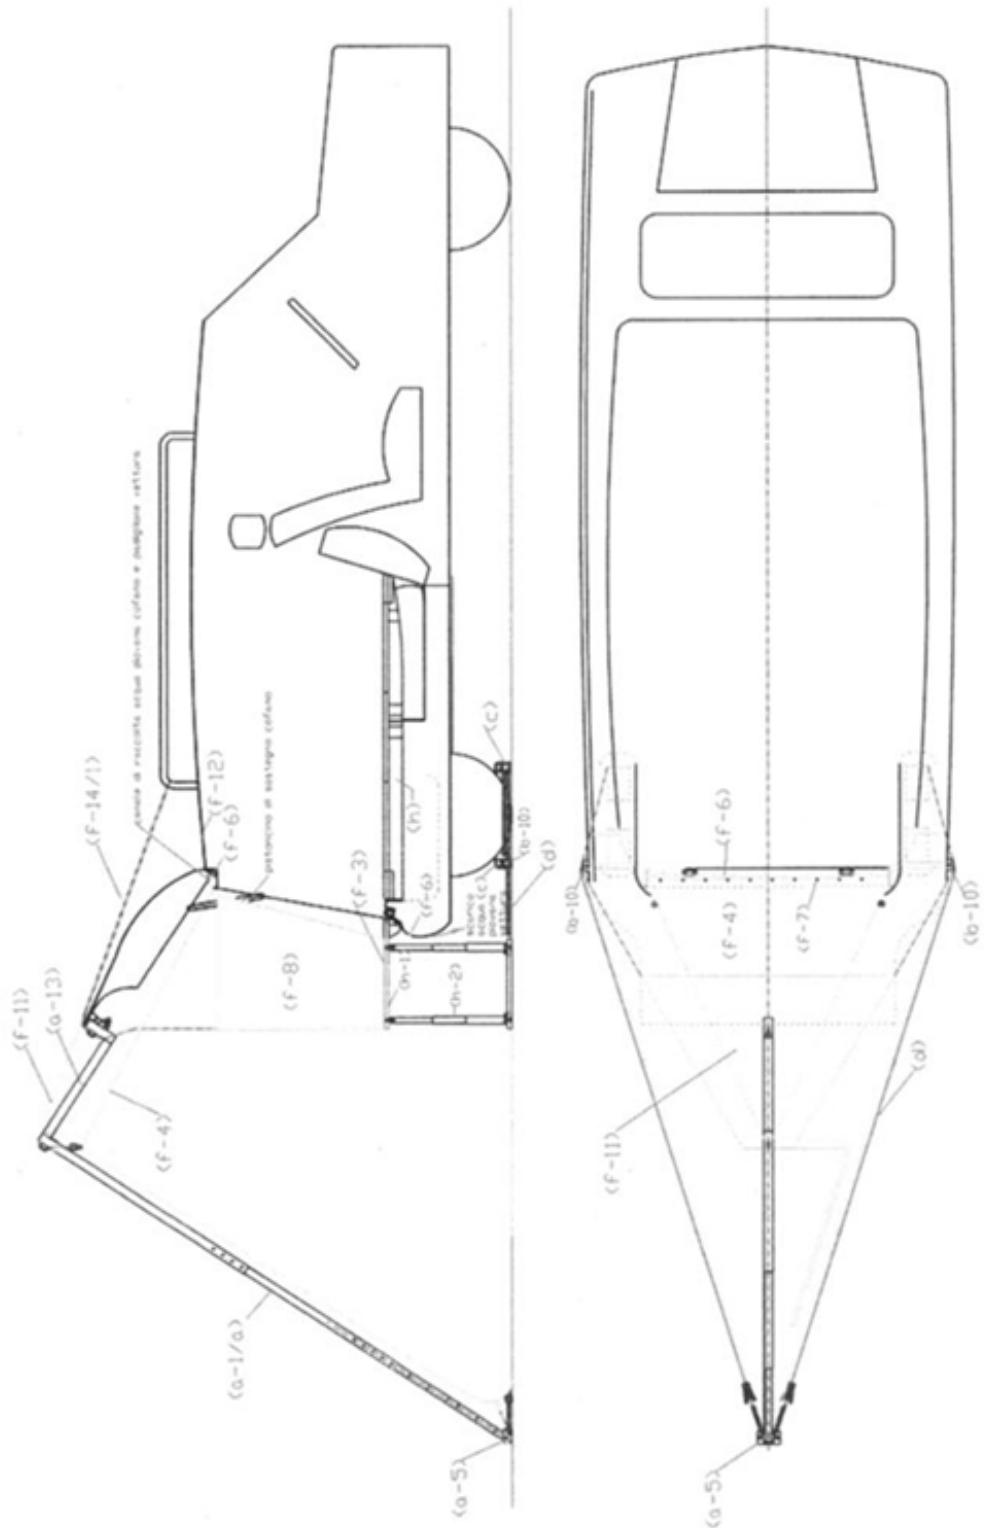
SEZIONE LONGITUDINALE E VISTA IN PIANTA TENDA CANADESE CON PROLUNGA PER VETTURA BASSA
